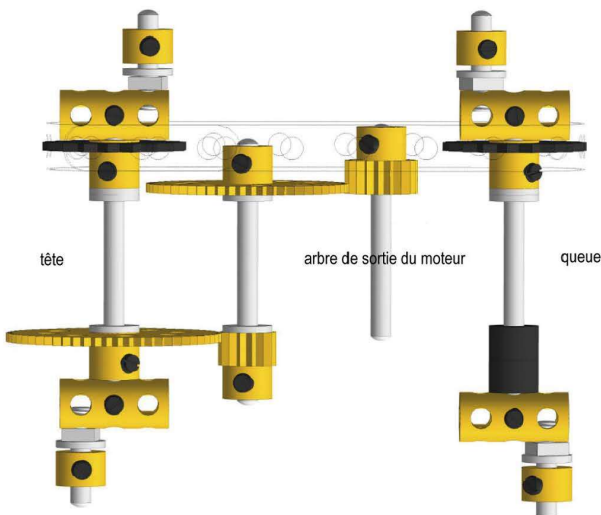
Le mécanisme vu de dessous, chaîne retirée
